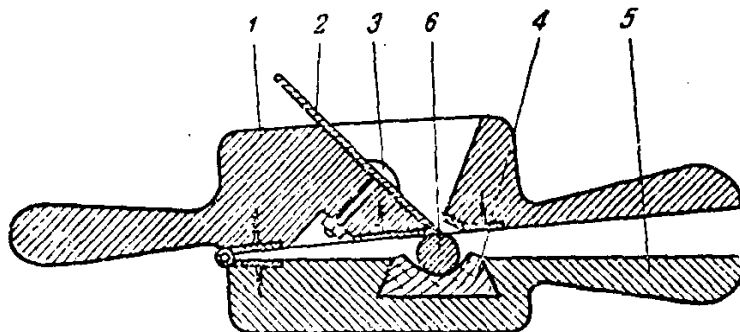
Приспособление для обработки деталей, имеющих конусность и кривизну по длине, на фрезерном станке.
